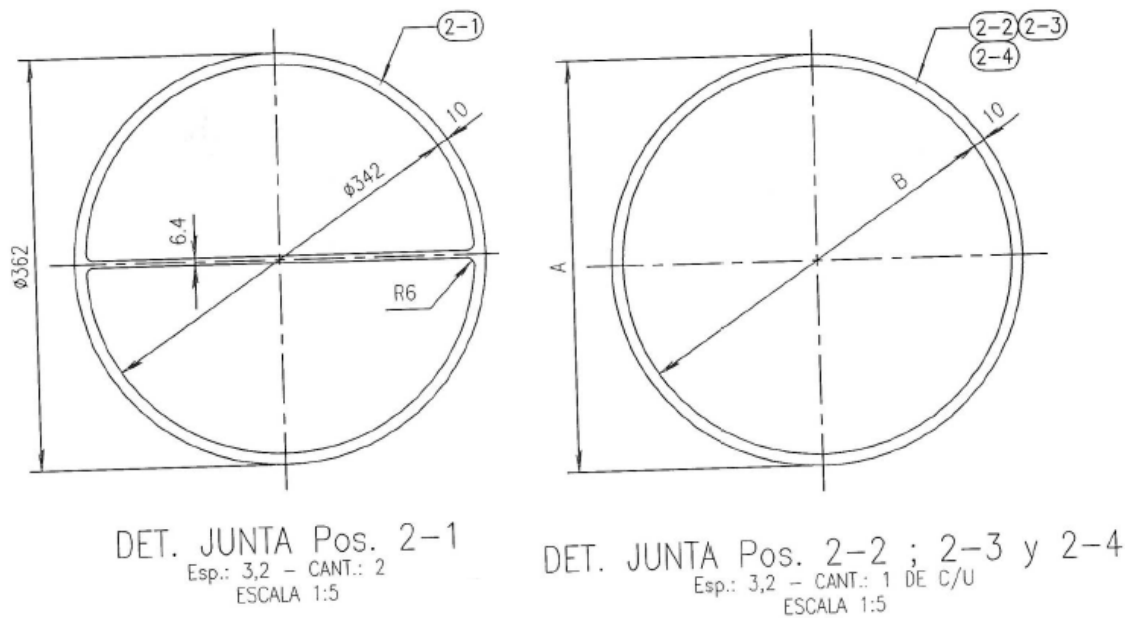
Plano de empaquetaduras enchaquetadas del 3I – 3205
